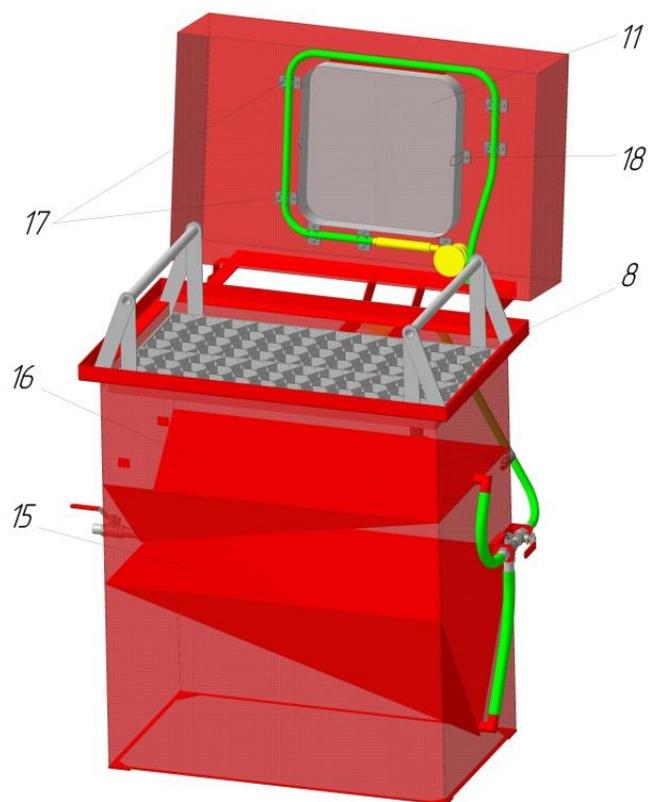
Общий вид установки (опорная площадка сверху)
